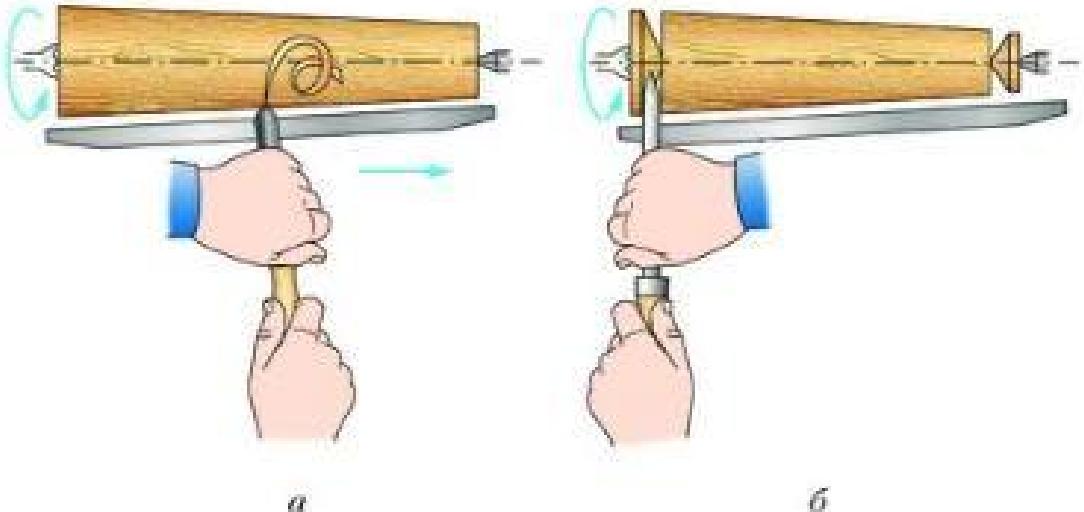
Обработка конической поверхности: *а* – обточка конуса; *б* – подрезка торца
